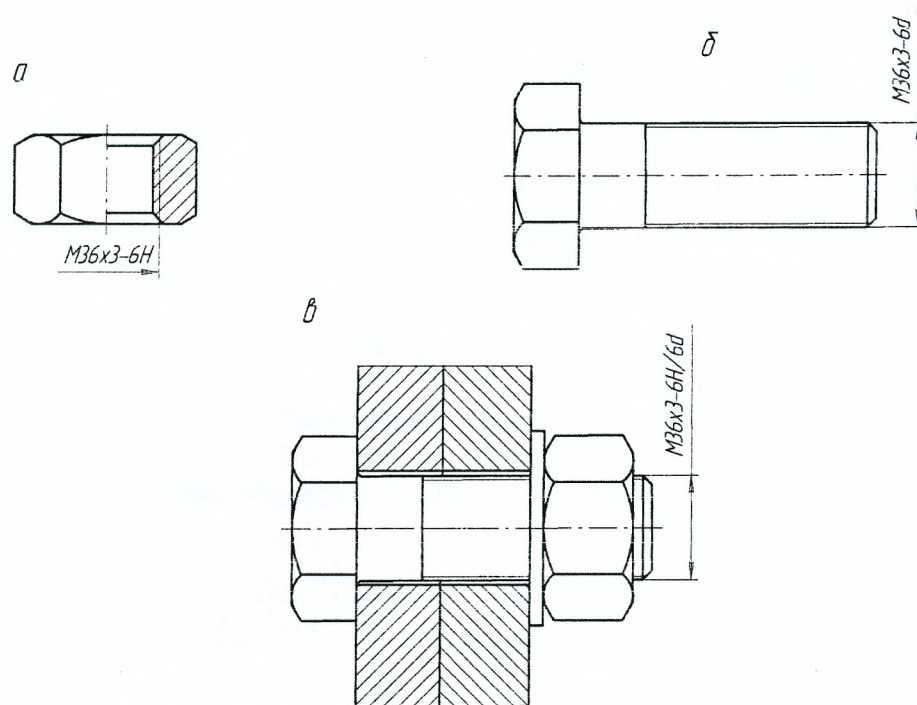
Условные чертежи: а – гайка; б – болт; в – резьбовое соединение
